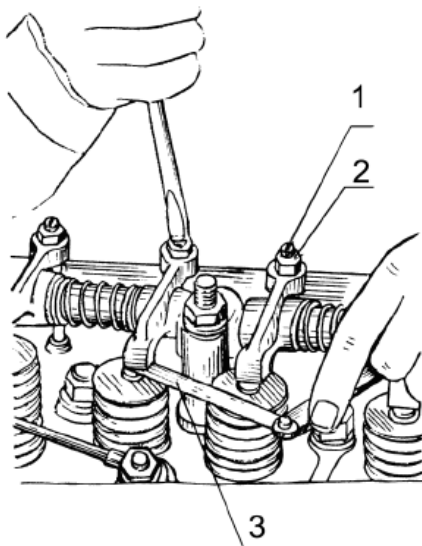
Регулировка зазора в клапанах двигателя Д-260:
